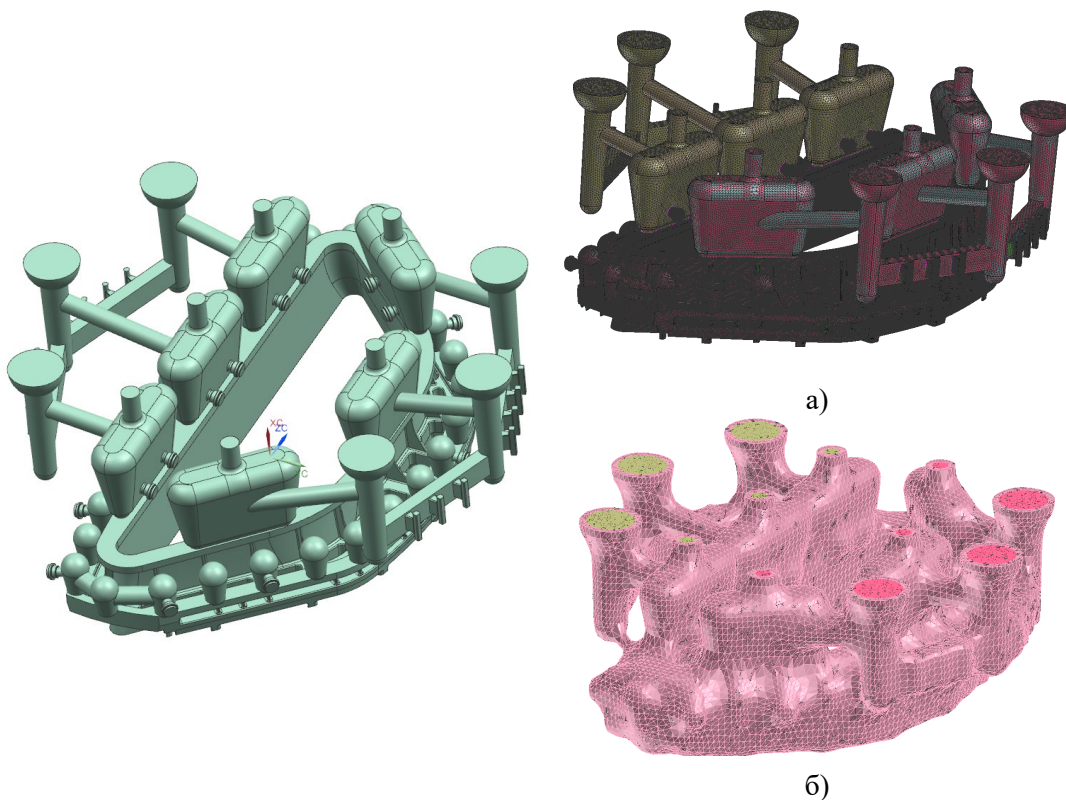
ЭГМ отливки детали «Корпус с фланцами».
